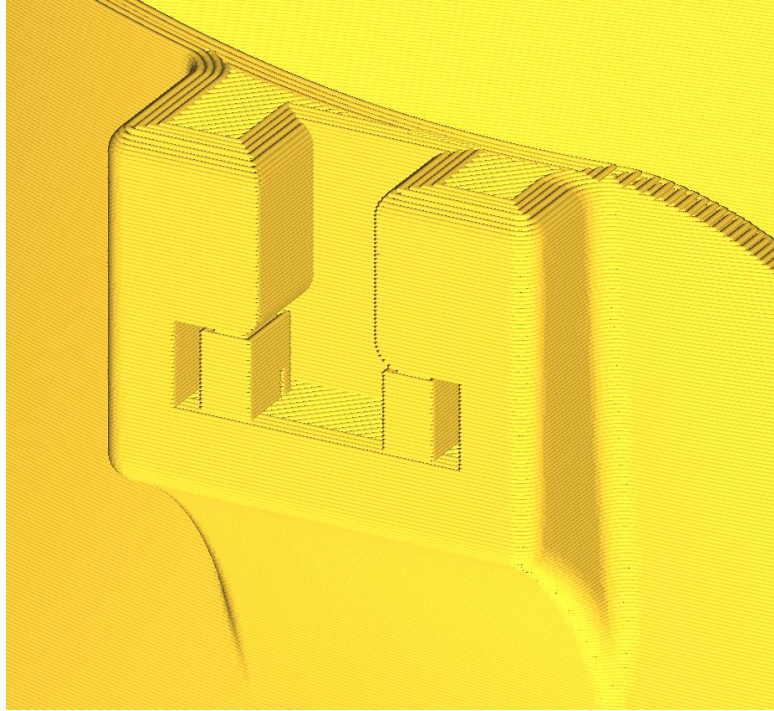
Material de soporte utilizado en la pieza de PLA.
